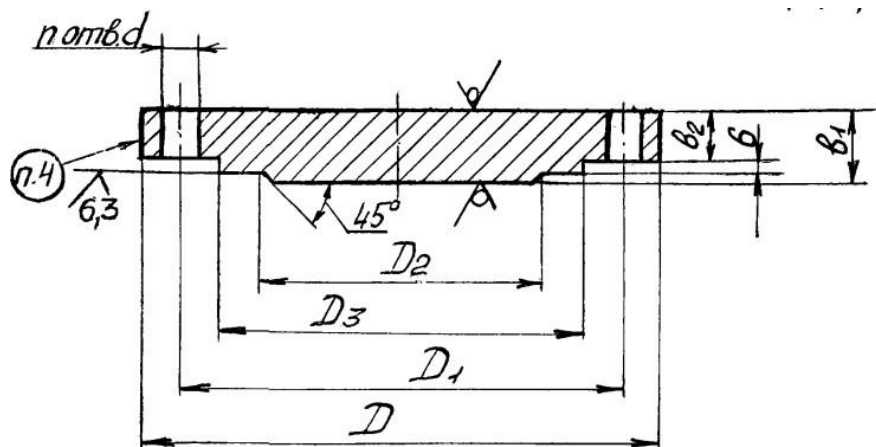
Расчетная схема плоской крышки корпуса [18]
